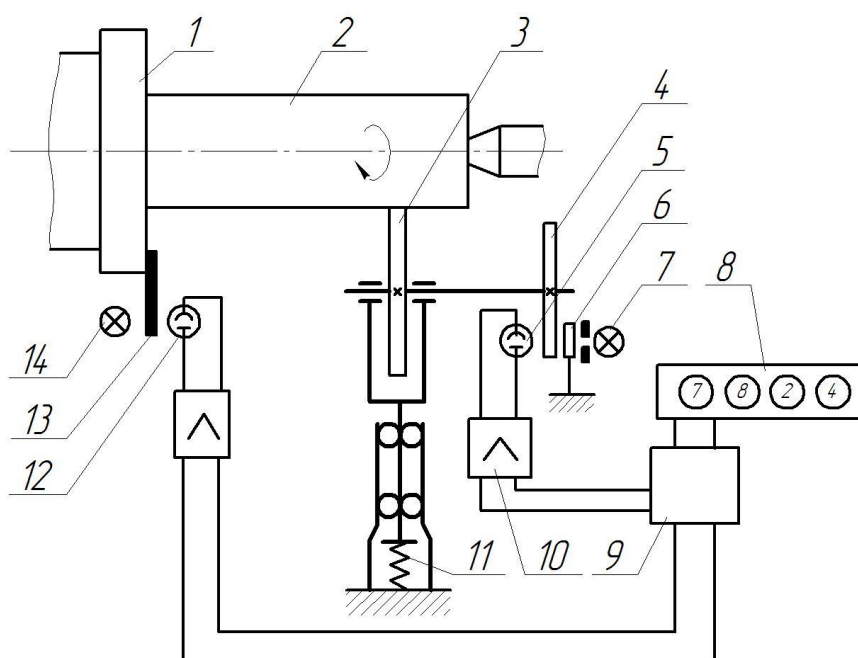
Принципова схема пристрою для контролю діаметрального розміру
